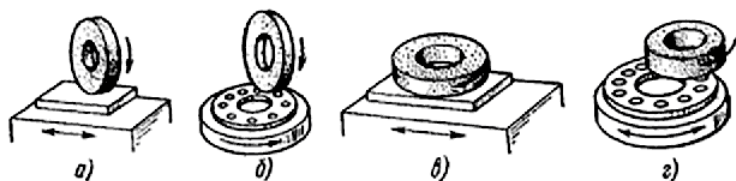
Основные схемы шлифования на плоскошлифовальных станках:
